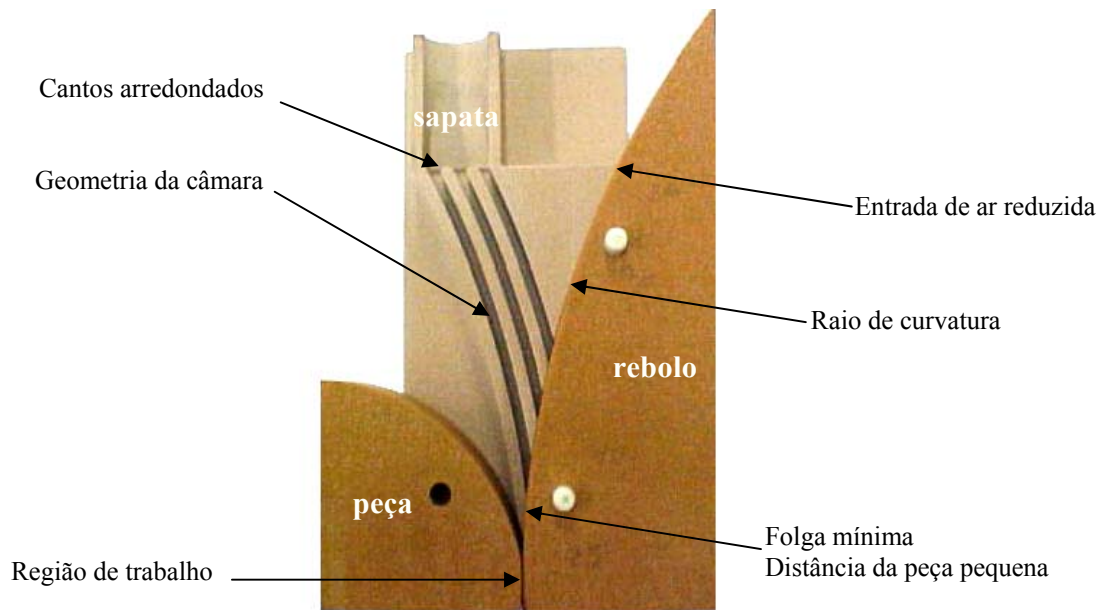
Protótipo em resina poliuretânica mostrando a montagem do conjunto tubeira, rebolo e peça.
